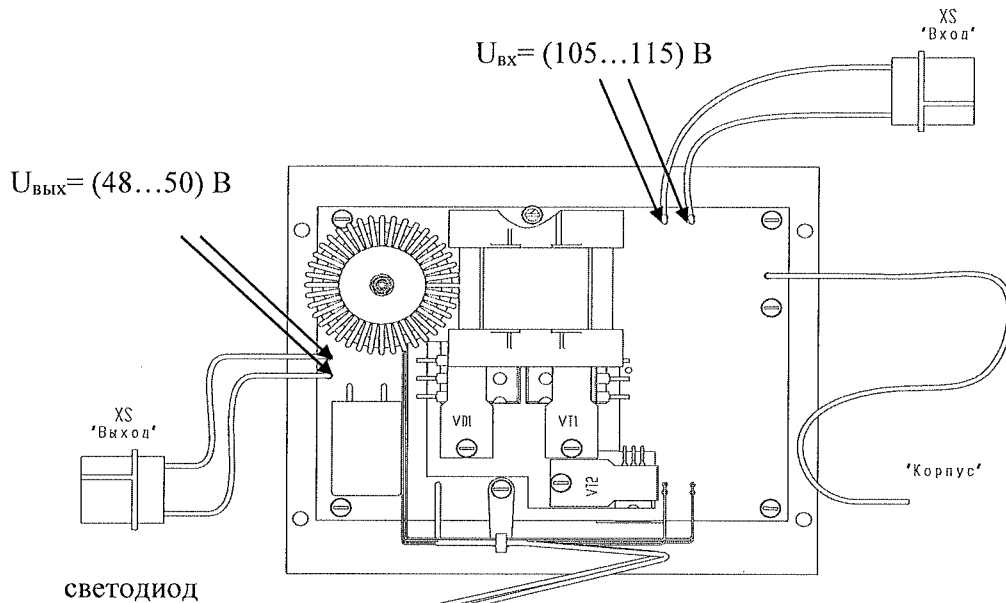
Сборочный чертеж канала АГБР.240.20.00.00
